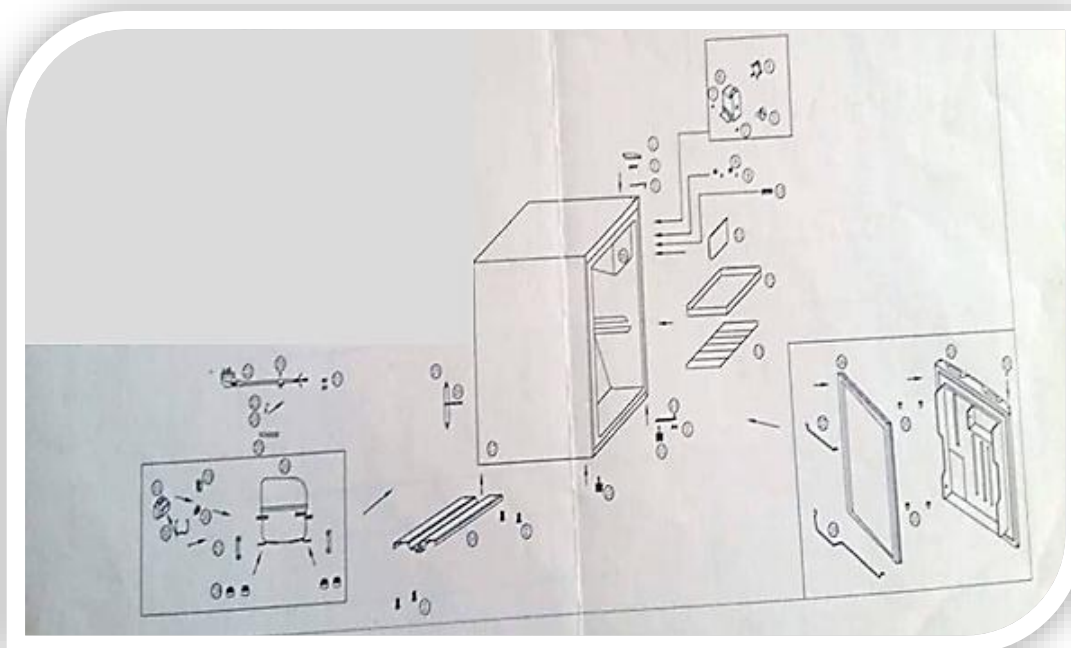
Vue éclatée du réfrigérateur (ENIEM)
